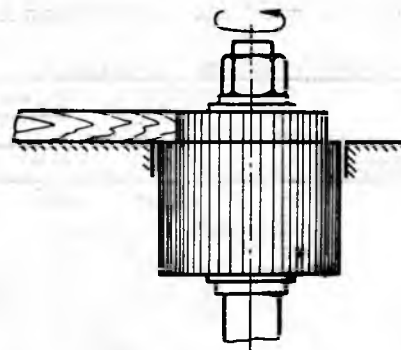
Лепестковый шлифовальный круг на фрезерном станке
